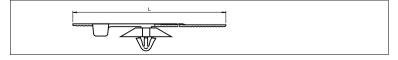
Abmessungszeichnung Kabelbinder
